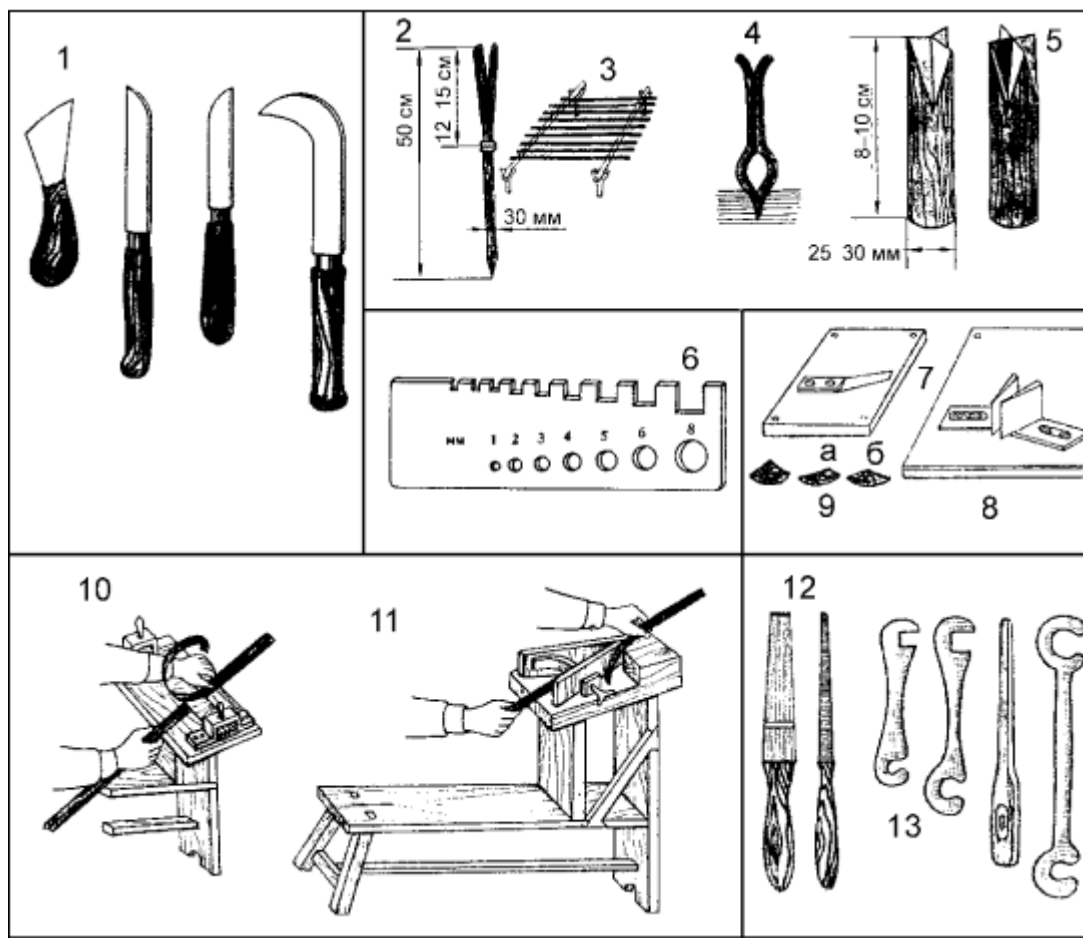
Инструменты для заготовки ивового прута и плетения:
